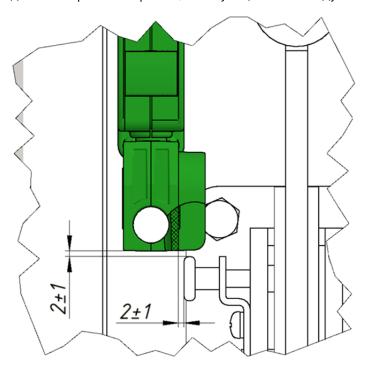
Установка блокиратора с разнесенными разъеденителями
